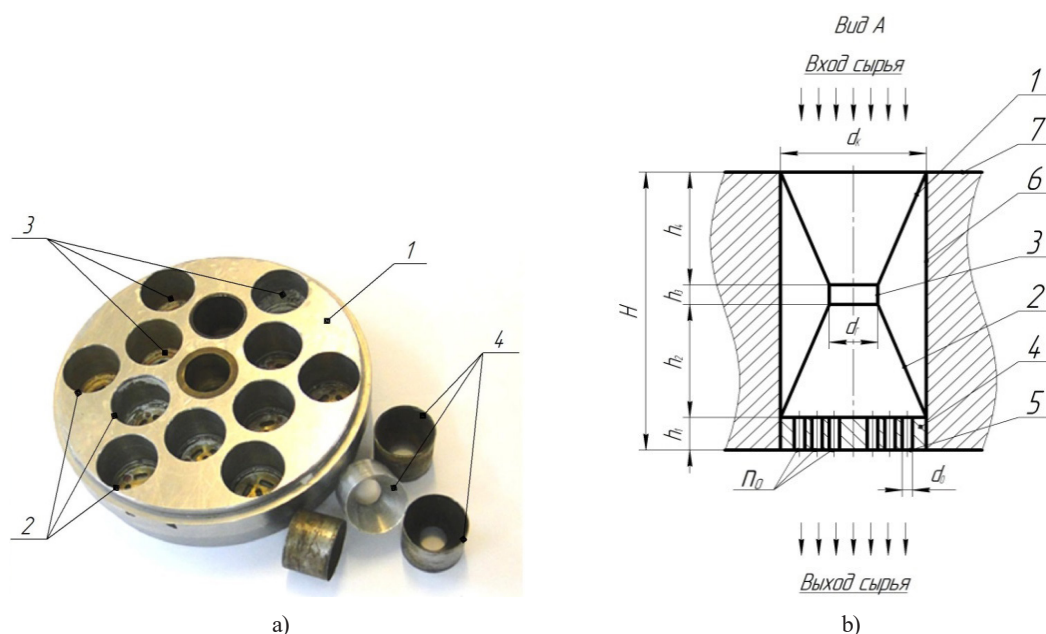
Общий вид (а) и конструктивная схема (б) матрицы с конфузорно-диффузорными вставками к малому макаронному прессу МИТ-2: 1 – матрица; 2 – колодцы; 3 – вкладыши; 4 – вставки. Стрелками указано направление движения исходного сырья
